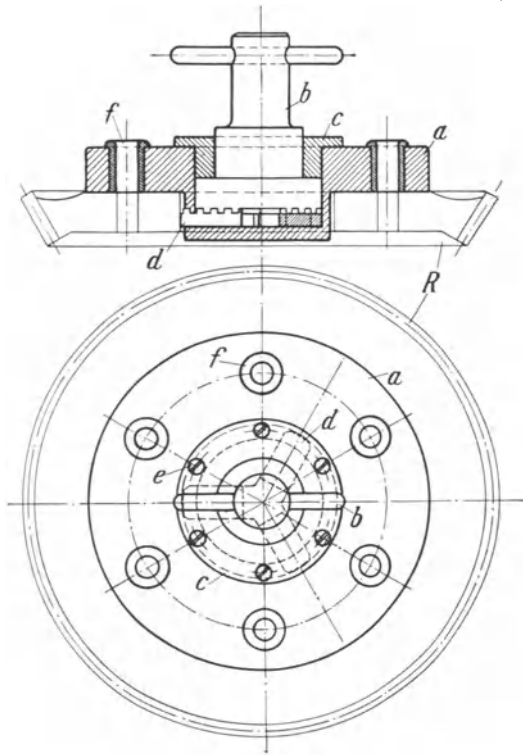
Bohrvorrichtung zum Bohren von Befestigungslöchern in Kegelrädern.
